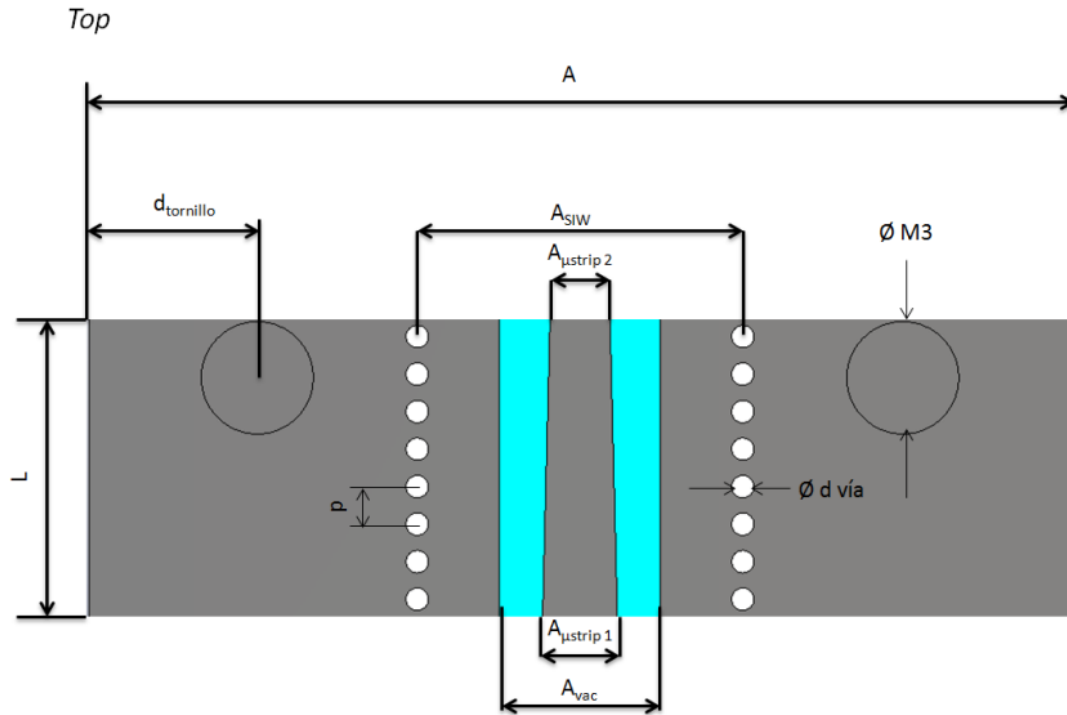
TRANSICIÓN SMA HORIZONTAL-MICROSTRIP-SIW APANTALLADA ACOTADA (TOP)
